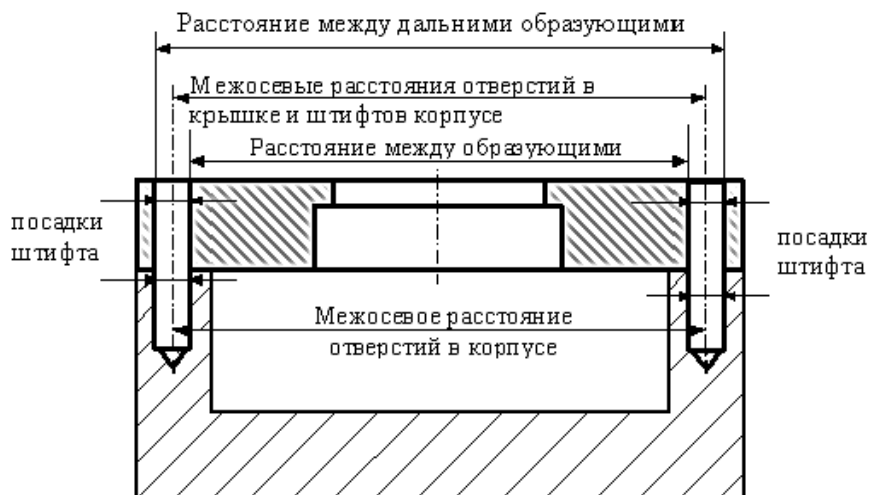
Эскиз соединения крышка-корпус (ориентирование по двум штифтам)
